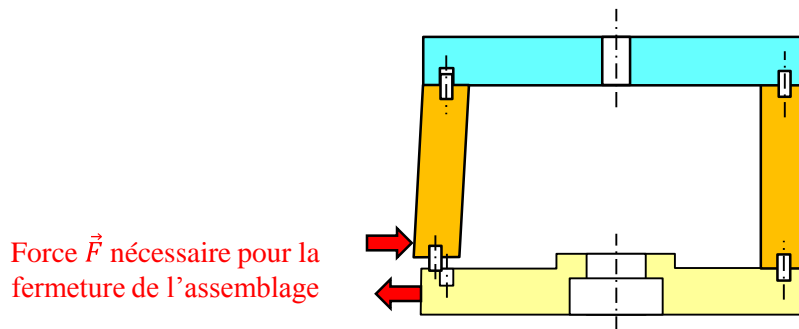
Efforts nécessaires pour fermer l'assemblage
